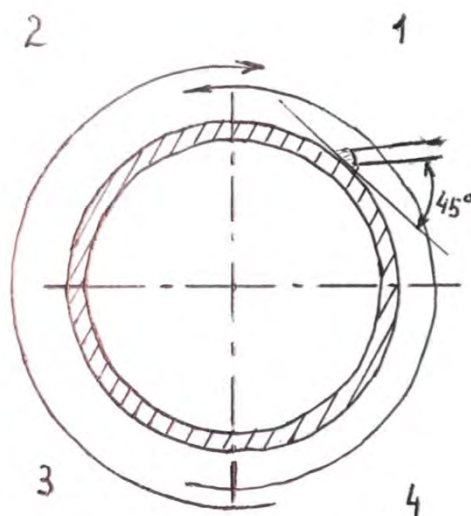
Последовательность сварки кольцевого шва трубы
